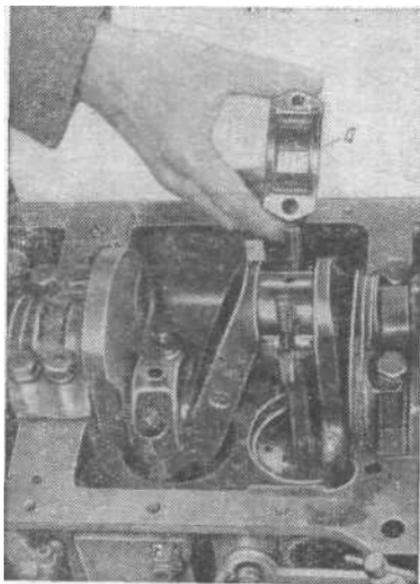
Укладка контрольной пластинки-щупа в шатунный подшипник:
